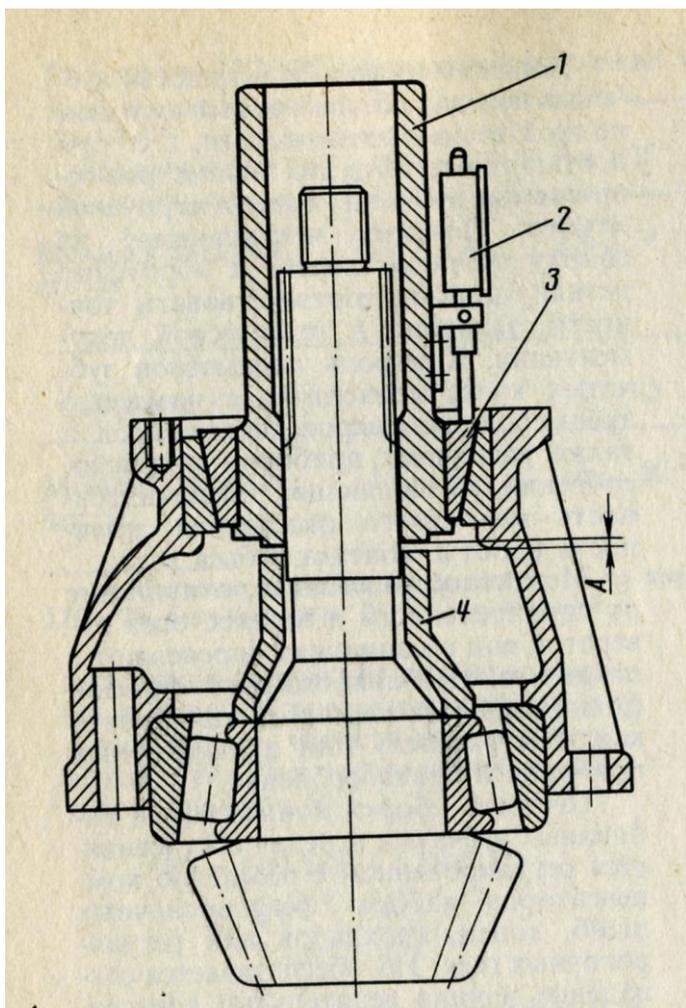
Приспособление для подбора толщины комплекта
